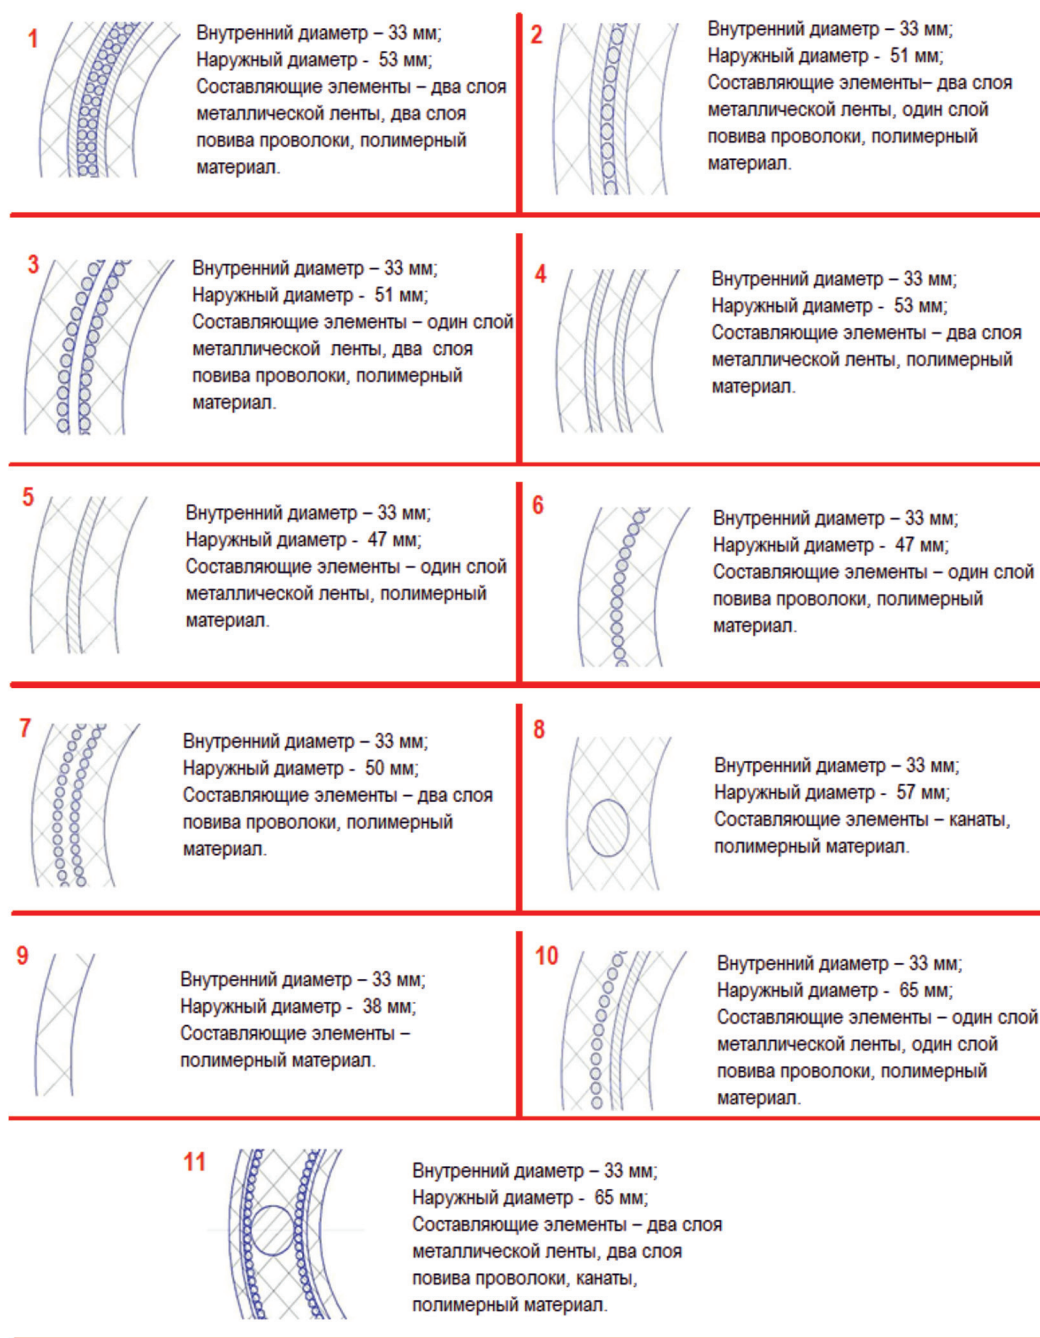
Варианты металлополимерной колтюбинговой трубы
